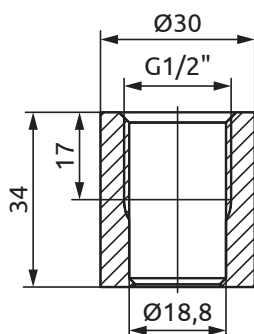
Габаритный чертёж варисторного nipples EL10662SS6L
